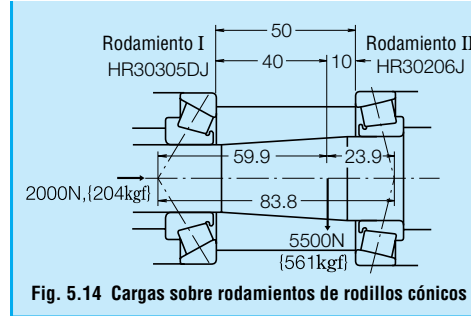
Cargas sobre rodamientos de rodillos cónicos
